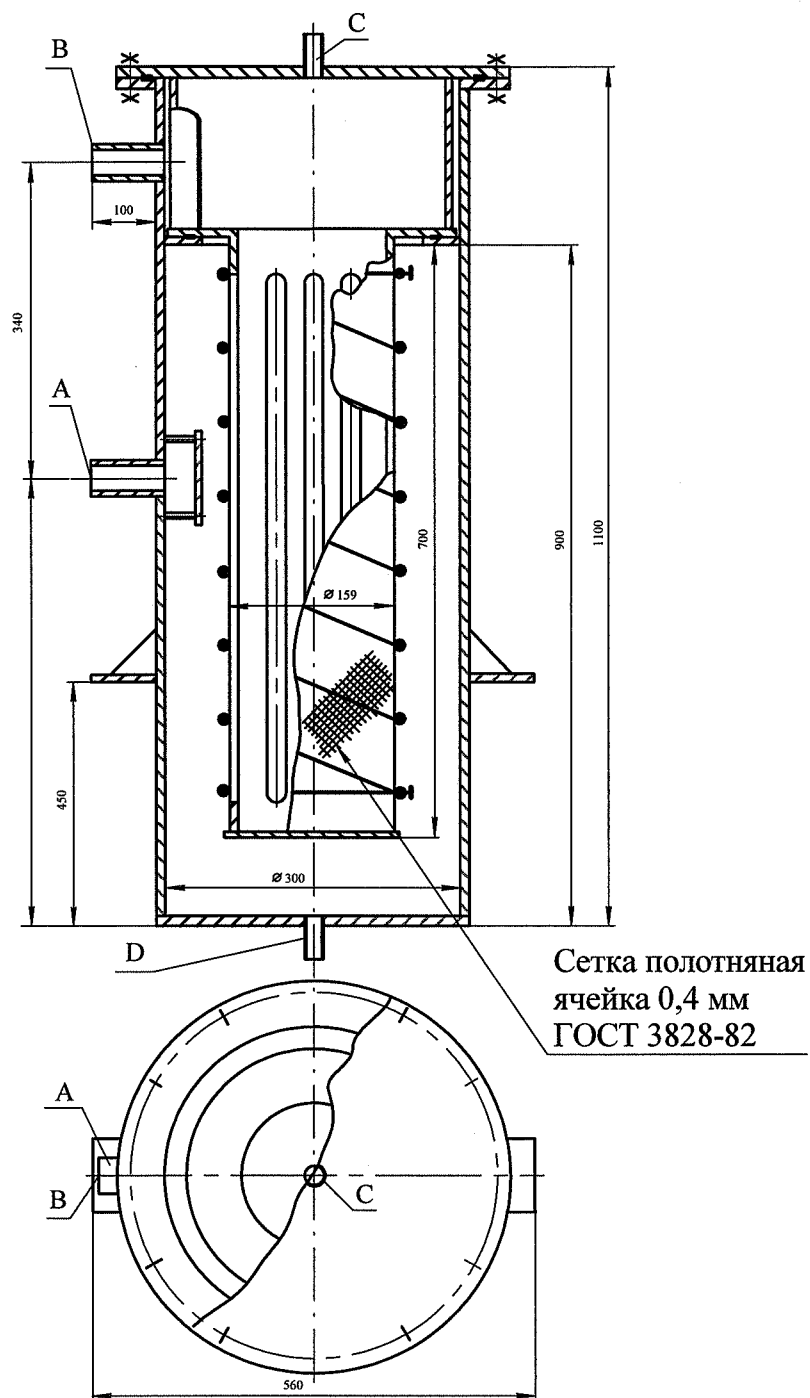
Габаритный чертеж фильтра самоочищающегося РСС11АТ101
